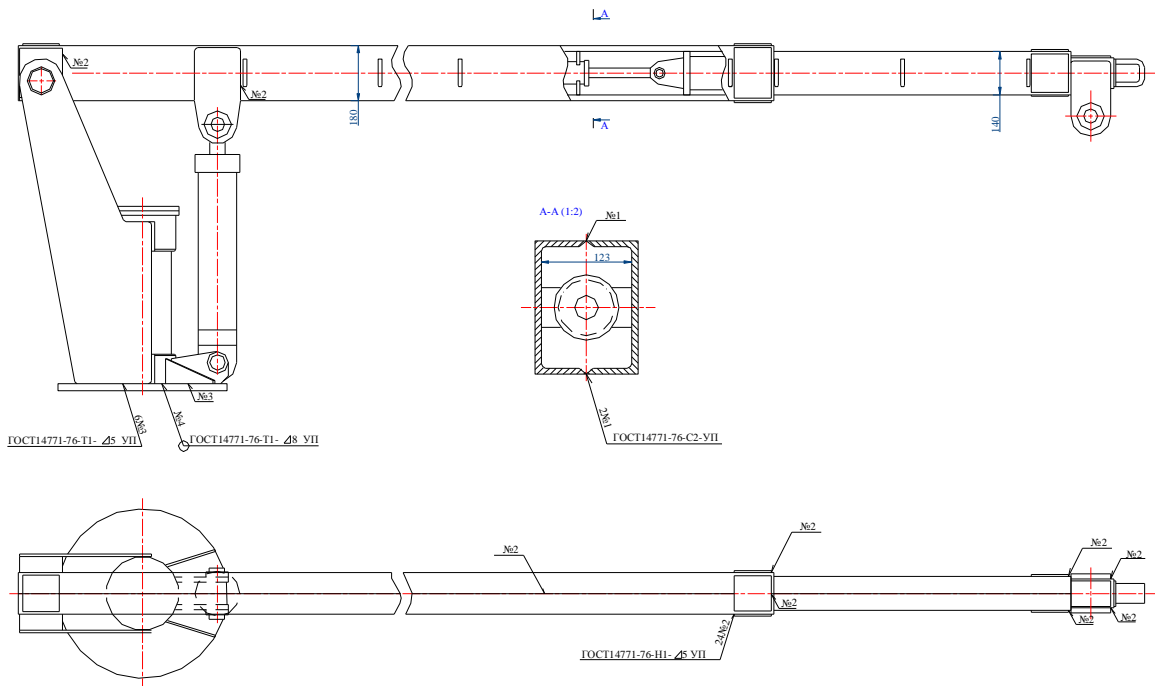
Сварные соединения конструкции стрелы.
